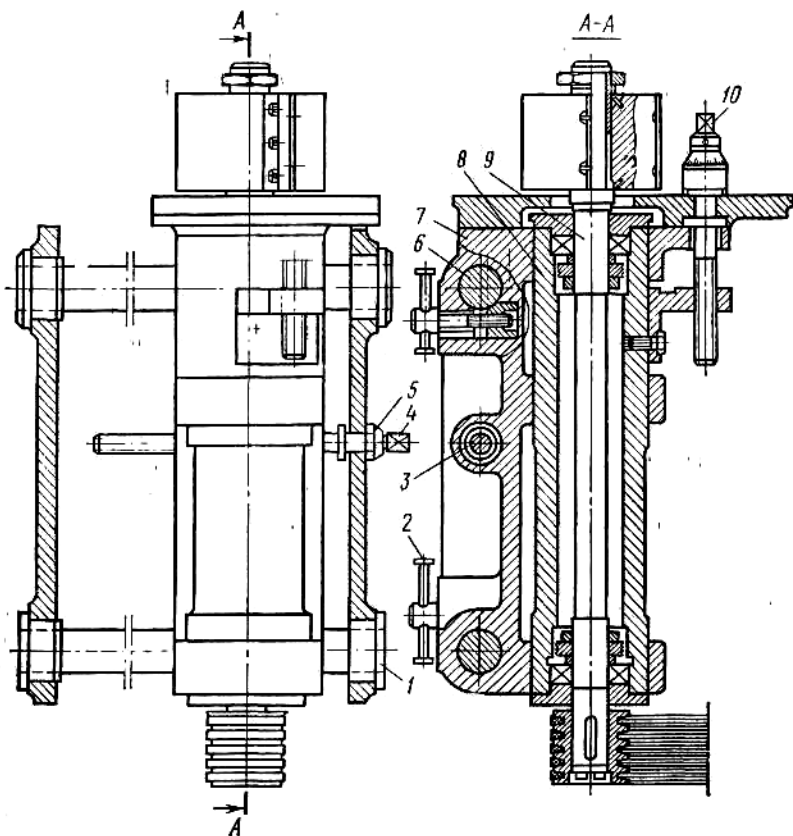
Суппорт вертикального шпинделя четырехстороннего продольно-фрезерного станка С26-2М:
